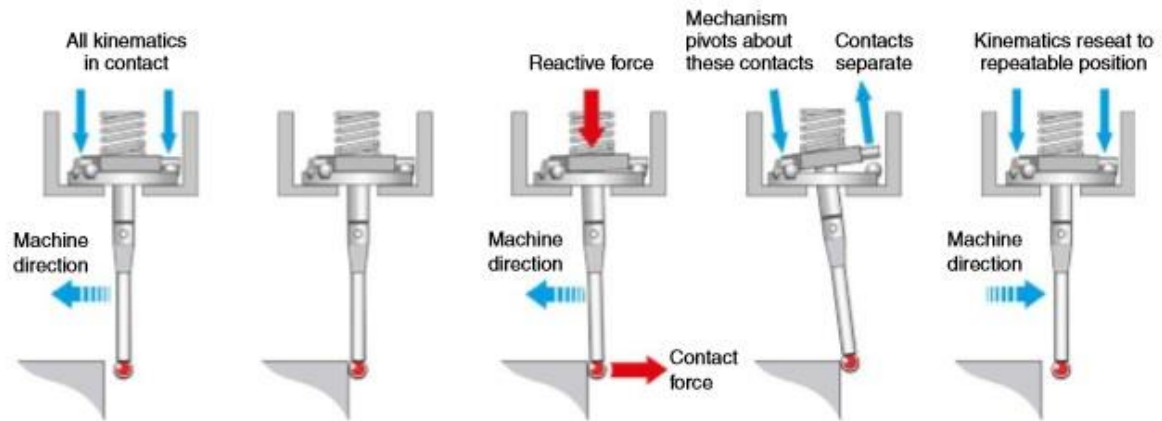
Etapas por que passa a ponteira durante a aproximação e contacto com uma peça (Renishaw, Probing Systems for CNC Machine Tools, 2014)
